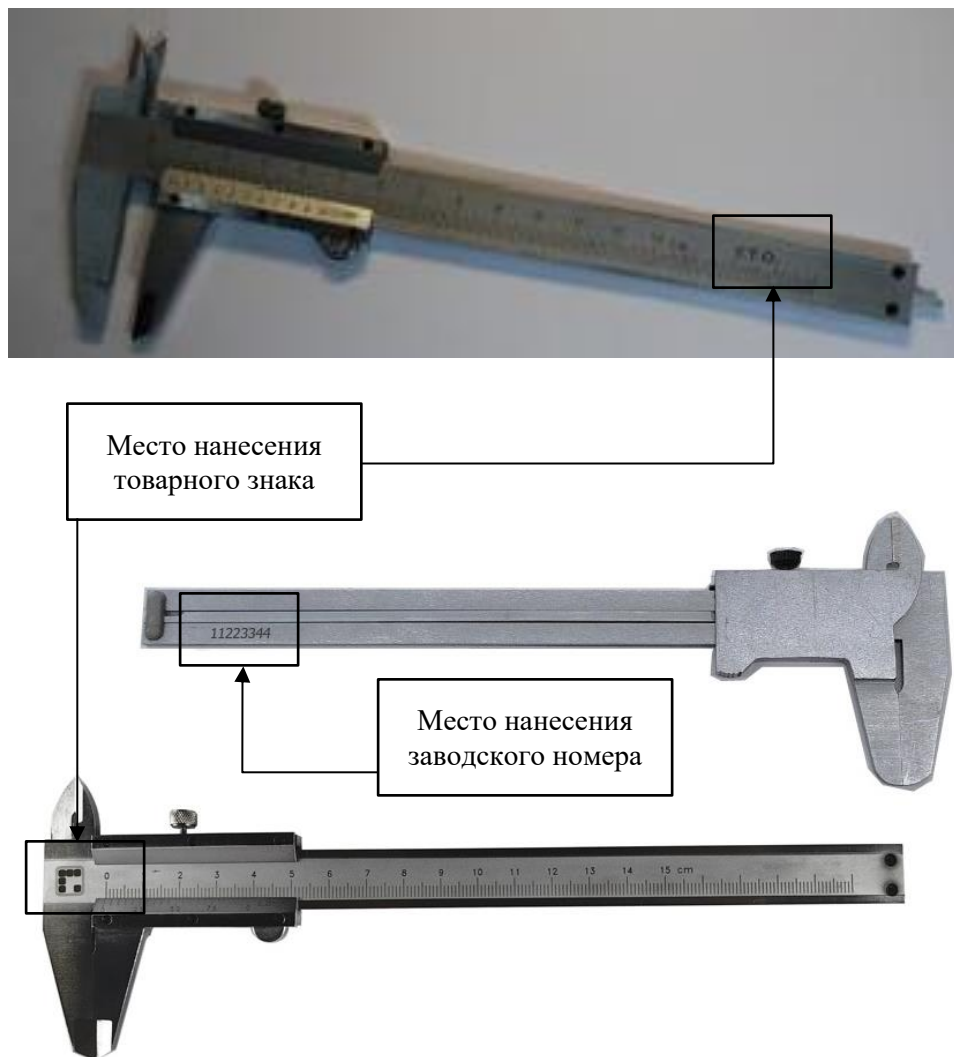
Общий вид штангенциркулей нониусных с глубиномером
